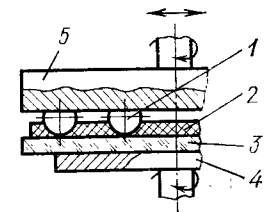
Изготовление плоской поверхности у шариковых заготовок
